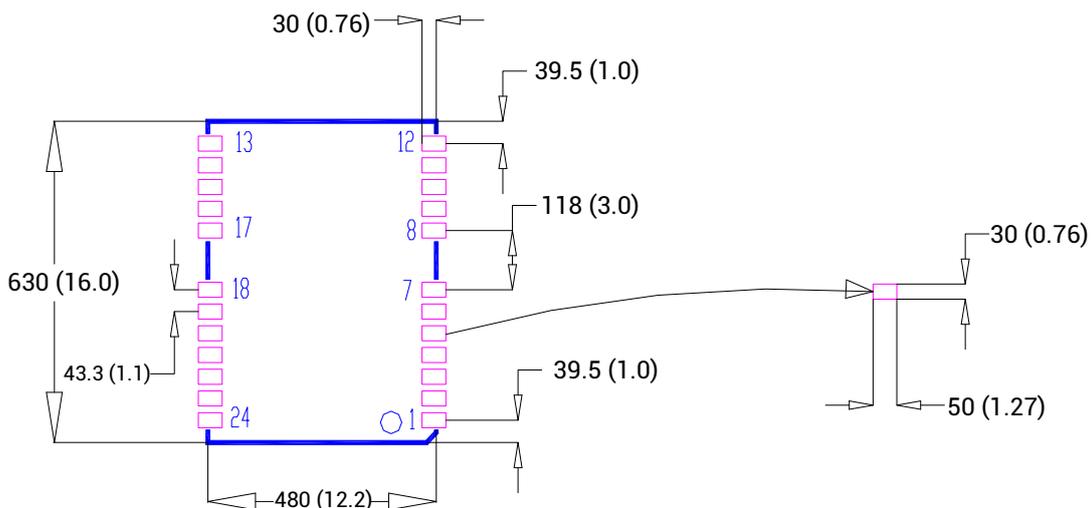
UM620N 模块推荐 PCB 封装设计 (尺寸单位: mil, 括号内单位: mm)
